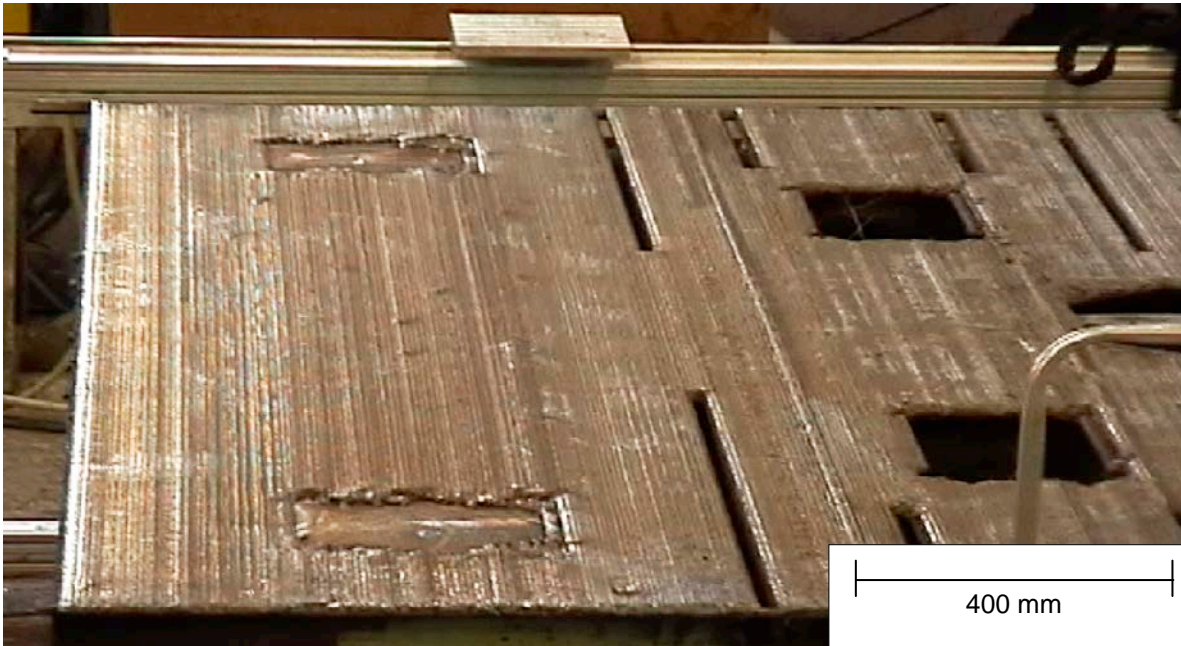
Bauteil mit großflächiger Beschichtung (2,0 x 1,8 m)
